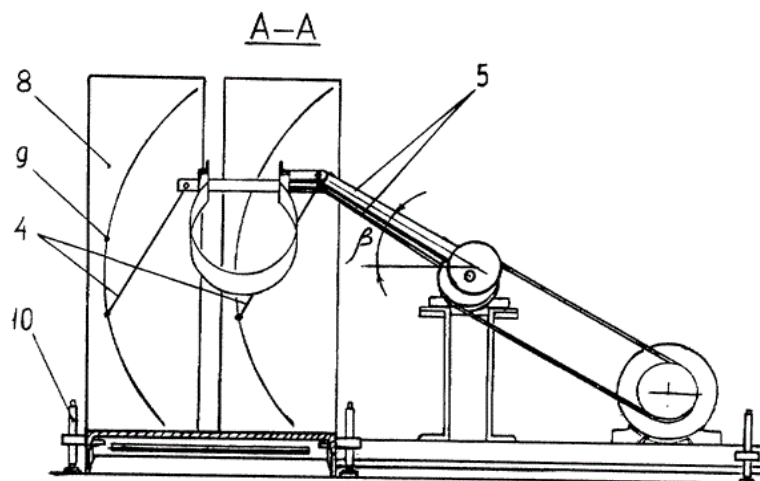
Вибрационный смеситель №3. Сечение А-А: 4 — рессоры; 5 — шатуны; 8 — стойки; 9 — регулировочные пазы; 10 — приспособление регулировки угла наклона
